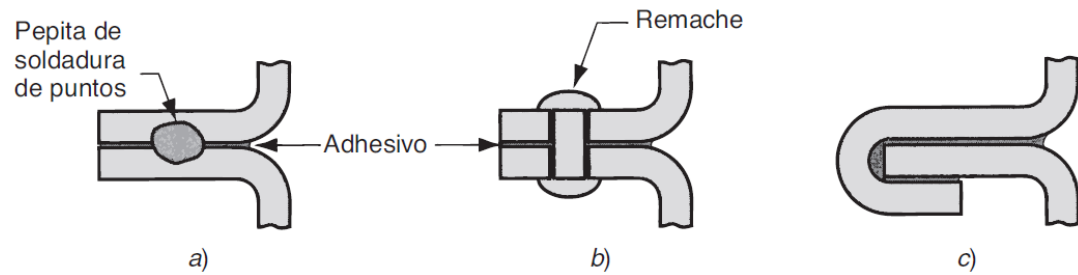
Pegado adhesivo combinado con otros métodos: a) soldadura de puntos y pegado adhesivo (adhesivo soldado); b) atornillado y pegado adhesivo y c) formado y pegado adhesivo [6].
